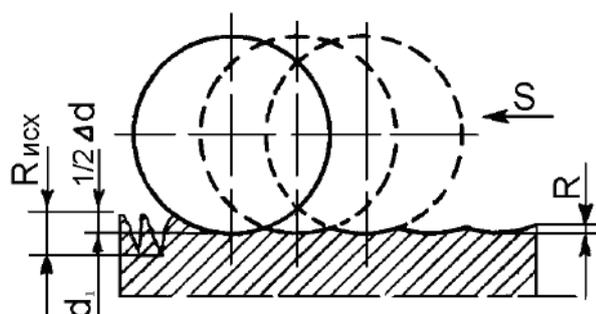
Схема обработки поверхности металла шариком.
